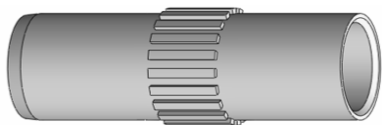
Напірна труба з виконаними на її зовнішній поверхні шліцами
